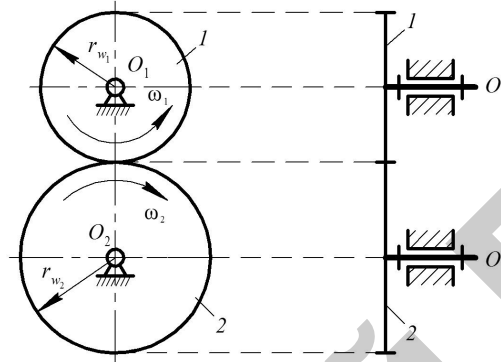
Схема зубчатой передачи с внешним зацеплением колес
